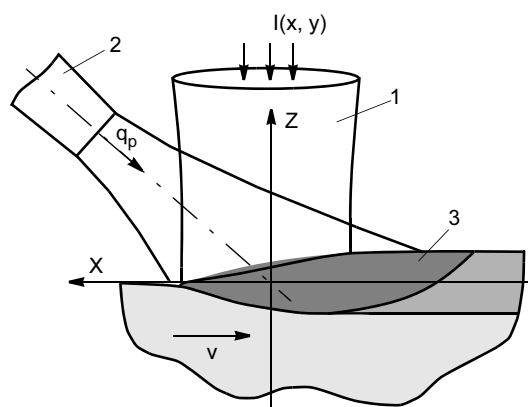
Схема лазерной порошковой наплавки: 1 — лазерный луч; 2 — сопло подачи порошка; 3 — ванна расплава
